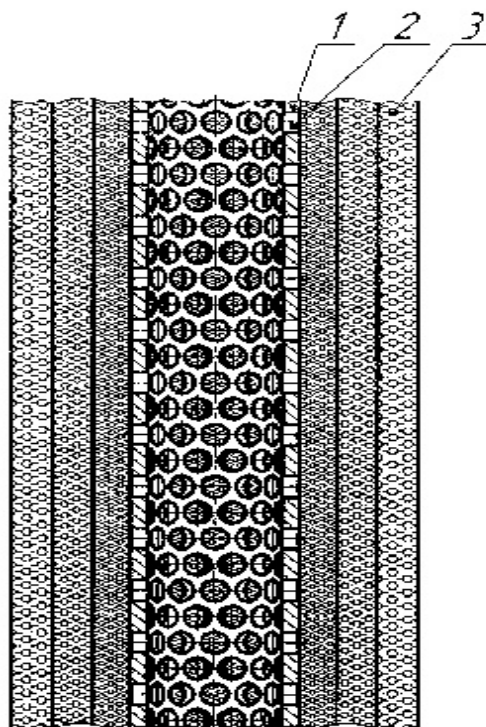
Фильтрующий элемент из пенометалла с уменьшающимся размером пор в радиальном направлении от наружной поверхности к внутренней
